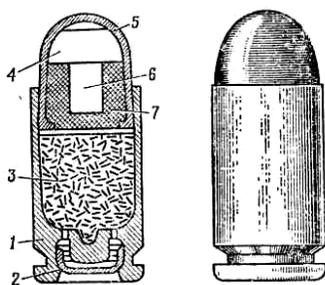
Общий вид 9-мм пистолетного патрона и его устройство:
